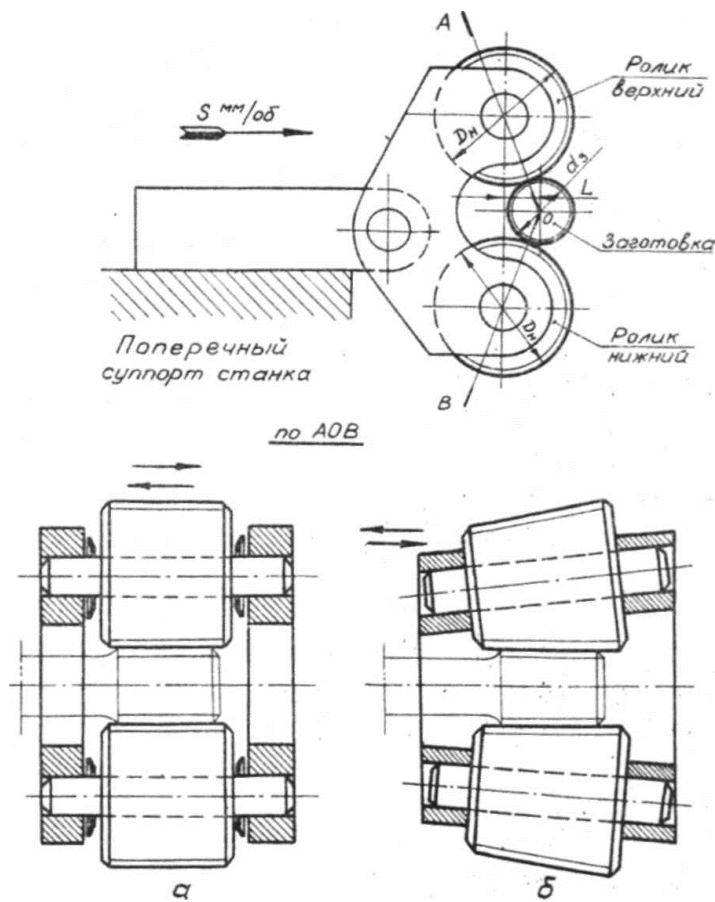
Обработка резьб тангенциальными резьбонакатными головками традиционного и адаптивного типа: а – традиционное накатывание цилиндрическими роликами; б – адаптивное накатывание коническими роликами.
